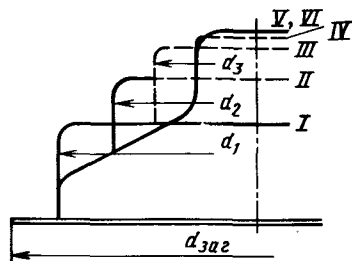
Схема штамповки-вытяжки входного конуса жаровой трубы камеры сгорания: IV — вытяжки; VI — калибрование
